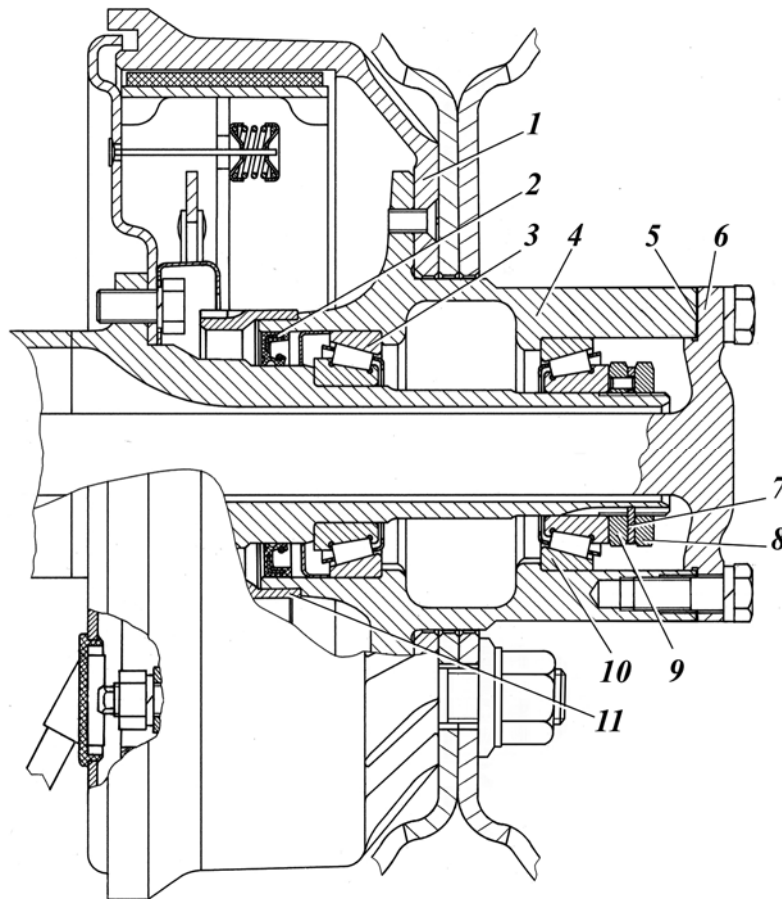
Ступица заднего колеса: 1 - тормозной барабан; 2 - манжета; 3 и 10 - подшипники; 4 - ступица; 5 - прокладка; 6 - полуось; 7 - замочная шайба; 8 - наружная гайка; 9 - гайка подшипников ступицы; 11 - ротор АБС
